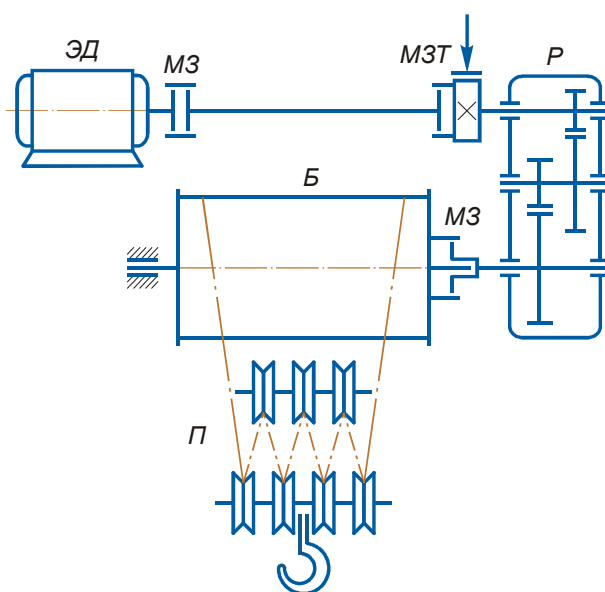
Кинематическая схема исходного механизма: ЭД — электродвигатель; МЗ — муфта зубчатая; МЗТ — муфта зубчатая с тормозным шкивом; Р — редуктор; Б — барабан; П — полиспаст с крюковой подвеской
